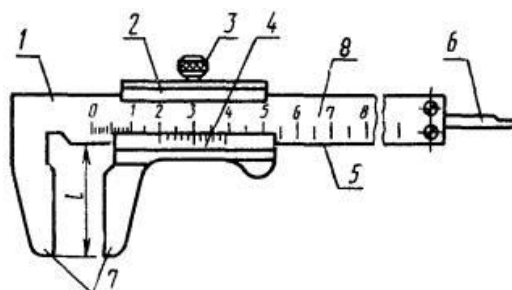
Односторонний штангенциркуль с глубиномером с измерительными поверхностями из твердых сплавов
